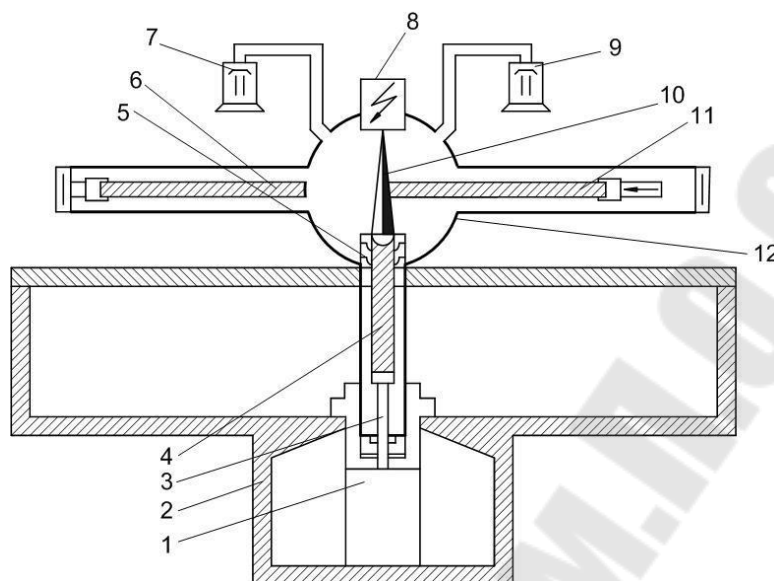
Схема электроннолучевой установки для вакуумного переплава металлов: 1- привод перемещения слитка; 2- корпус; 3- подвижный шток; 4- переплавленный слиток; 5- кристаллизатор; 6- резервный металл для переплавки; 7,9- насосы; 8- электронная пушка; 10- электронный луч; 11- переплавляемый металл; 12- вакуумная камера
